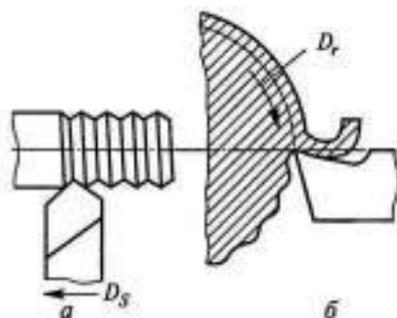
Образование поперечной (а) и продольной (б) шероховатости поверхности при токарной обработке:
